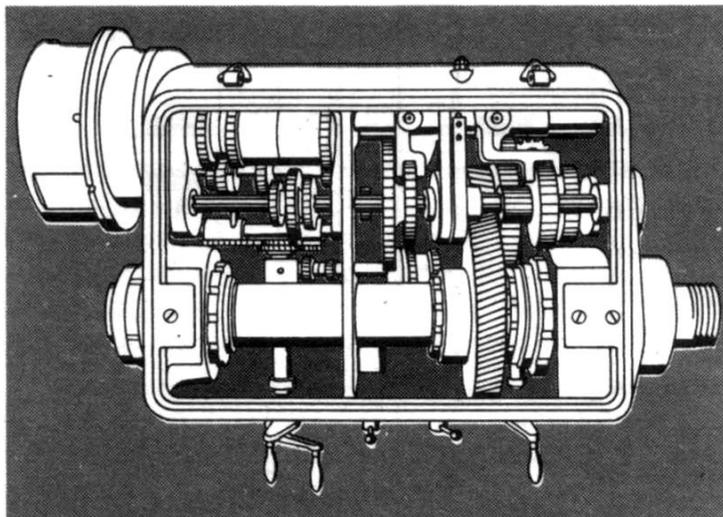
,1. Cabezal fijo con mecanismo de engranajes.
